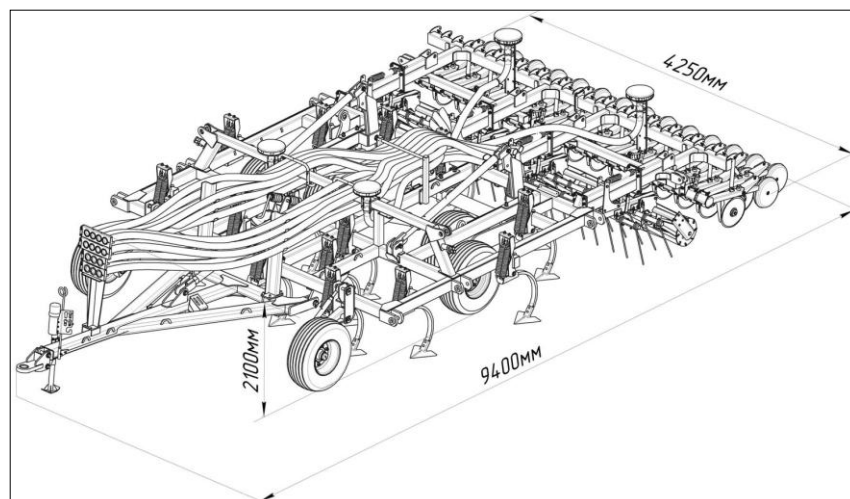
Вид центральной части культиваторной части комплекса при подготовке к транспортированию
